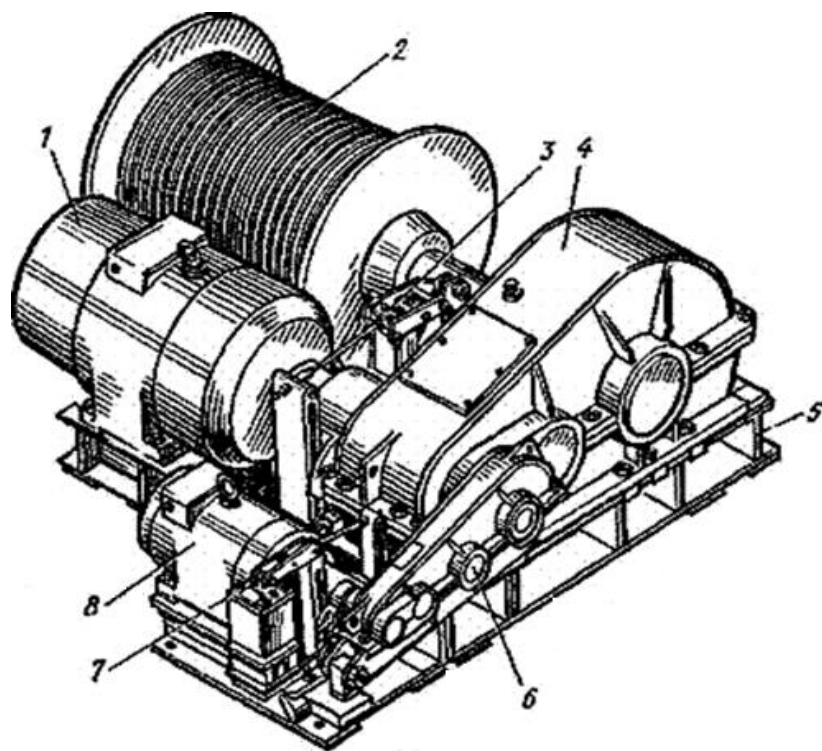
Грузовая лебедка основного подъема крана СКГ-40А: 1, 8 – электродвигатели; 2 – барабан; 3, 7 – электромагнитные тормоза; 4, 6 – редукторы; 5 – рама редуктора
